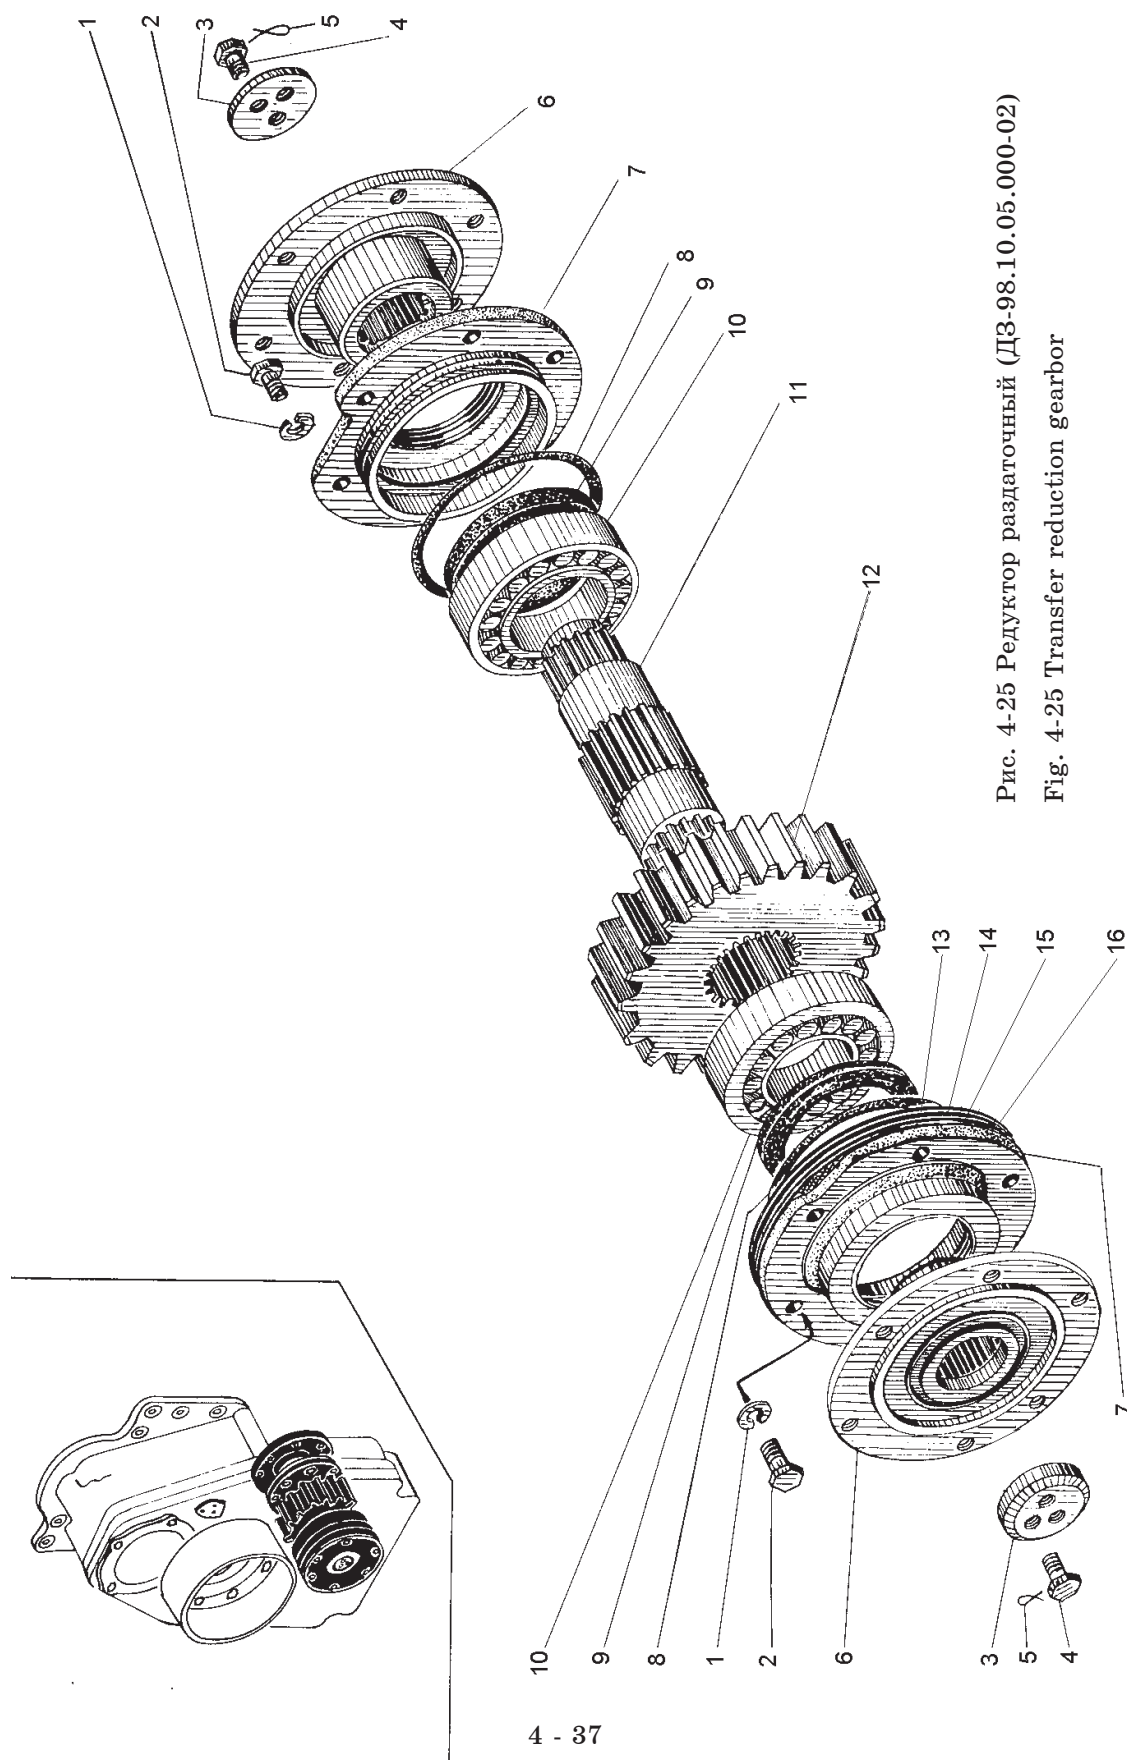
Редуктор раздаточный (ДЗ-98.10.05.000-02)
